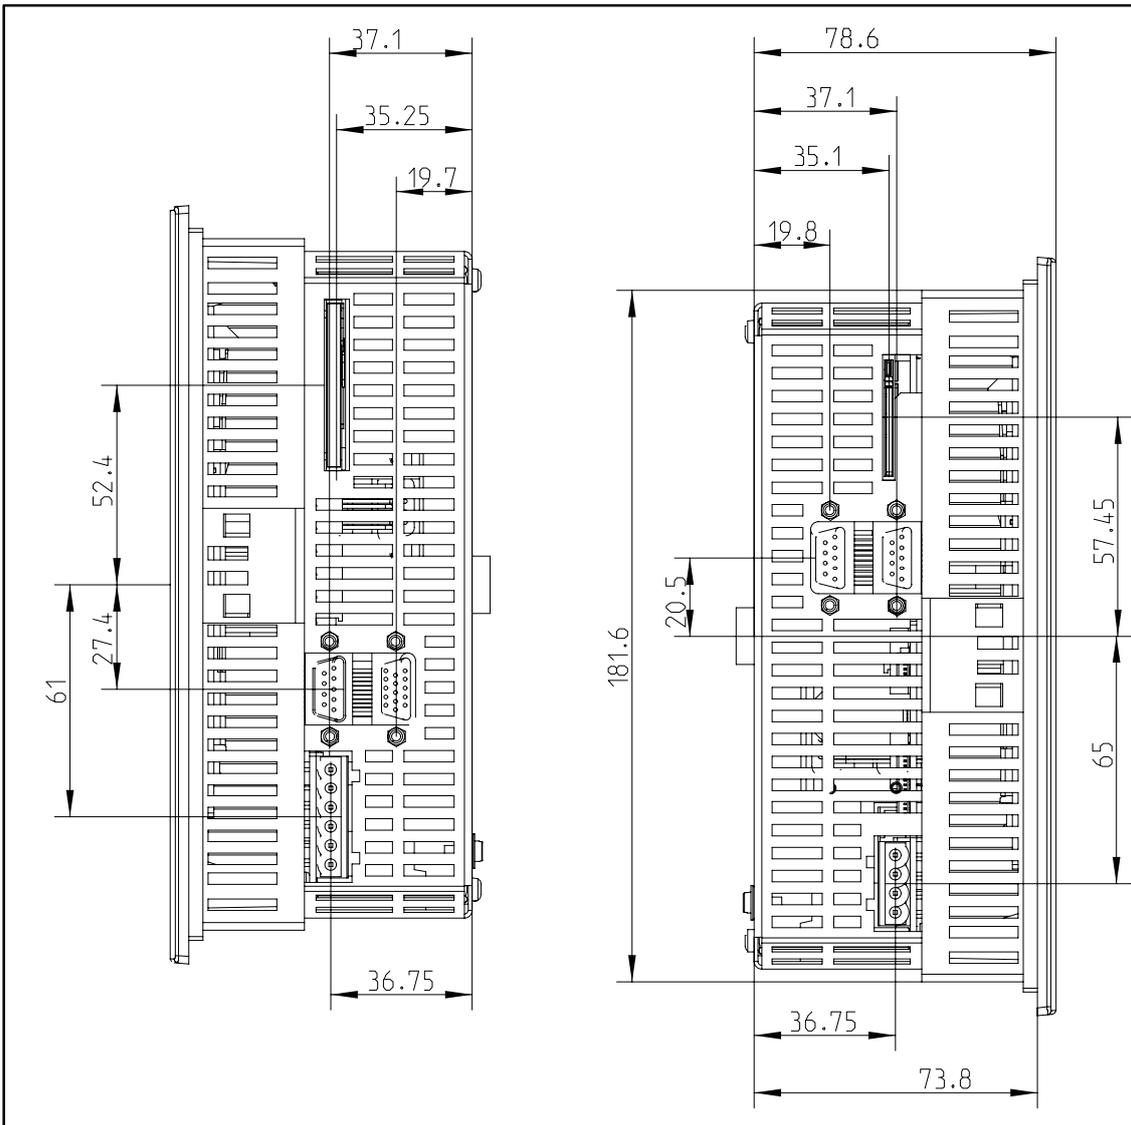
Maßbilder für das C7-635 Touch (Maße in Millimeter)
